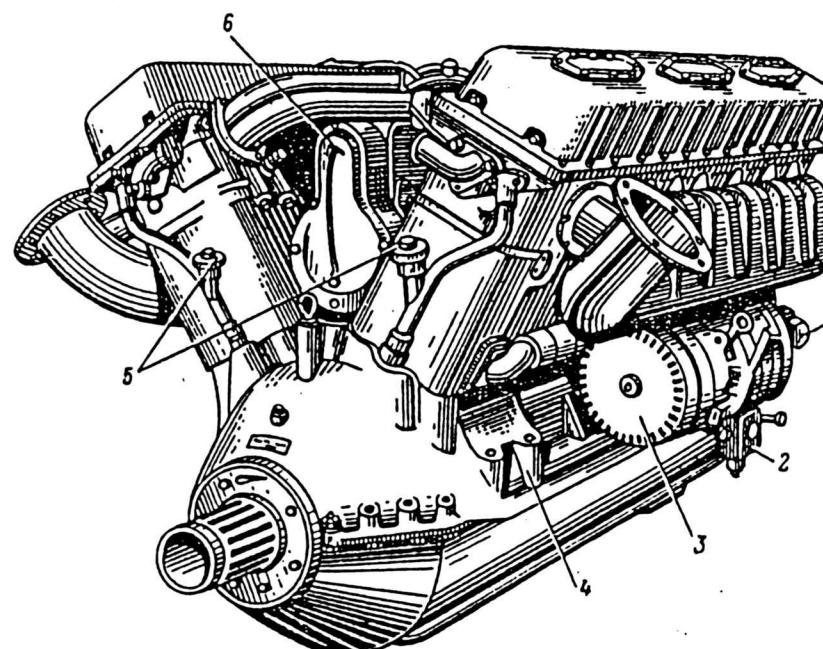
Двигатель В-54К-ИС (вид со стороны носка):
